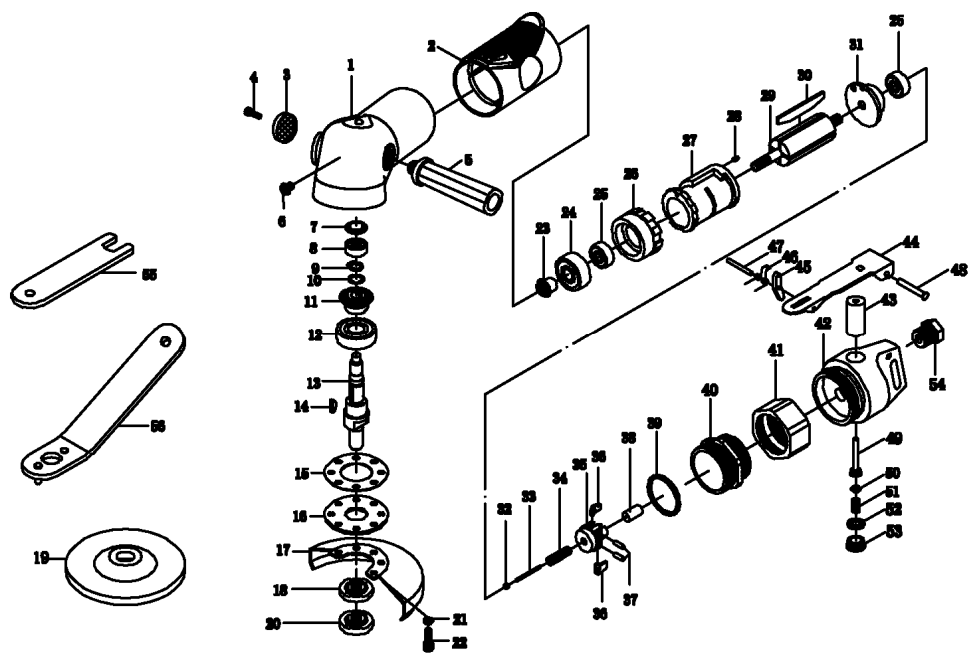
а. Схема устройства и сборки машины шлифовальной угловой пневматической MFG 125/001-2
